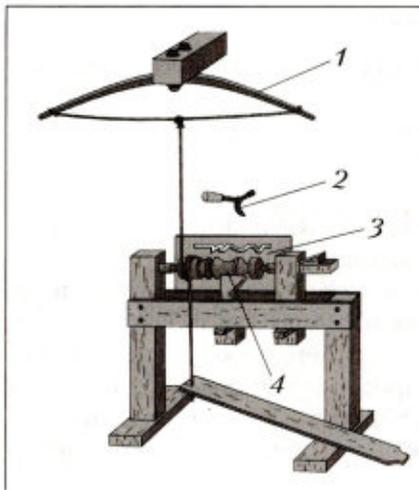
Станок с лучковым приводом: 1 – упругое звено (лучковый привод); 2 – инструмент, с помощью которого отслеживали форму шаблона и обрабатывали заготовку; 3 – шаблон (прорезь в стенке станины); 4 – заготовка
